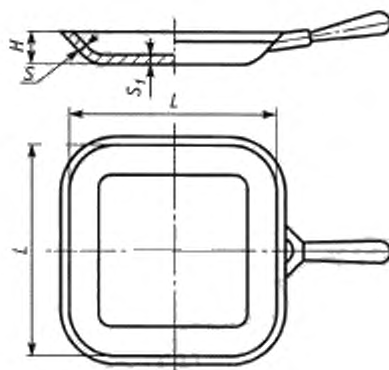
Сковорода квадратная без крышки и с одной ручкой
